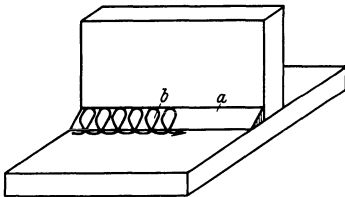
Elektrodenführung bei Kehlschweißung.
